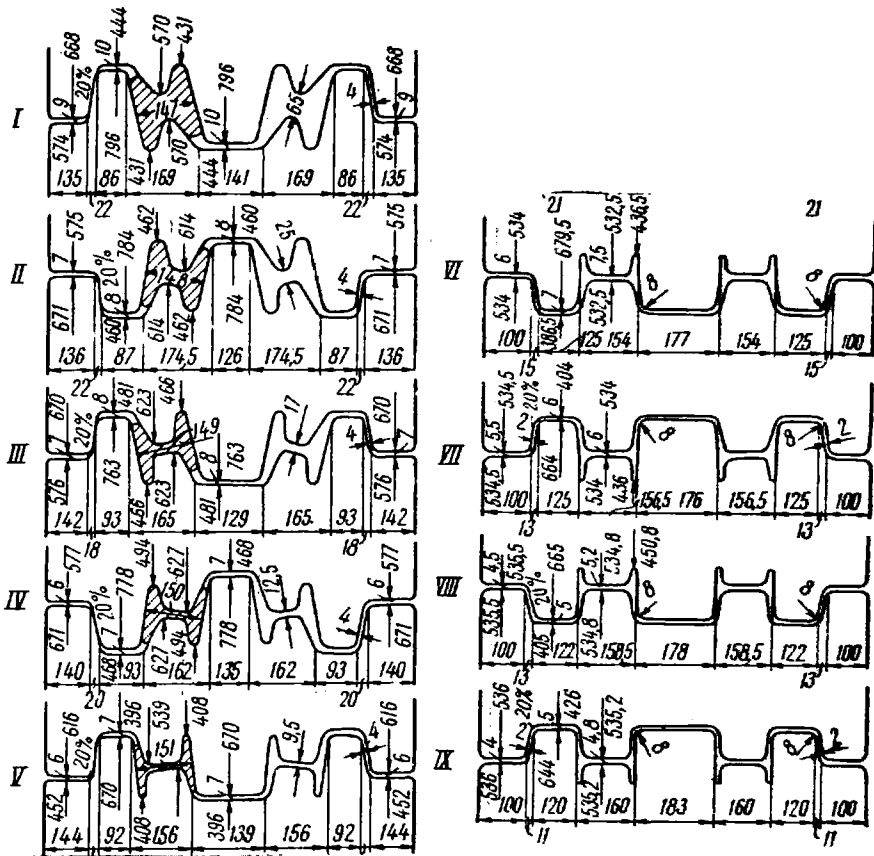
Калибровка валков для прокатки балки № 16 с косорасположенными калибрами (стан 500 кросс-коунтри; I—IX — номера клеток)
